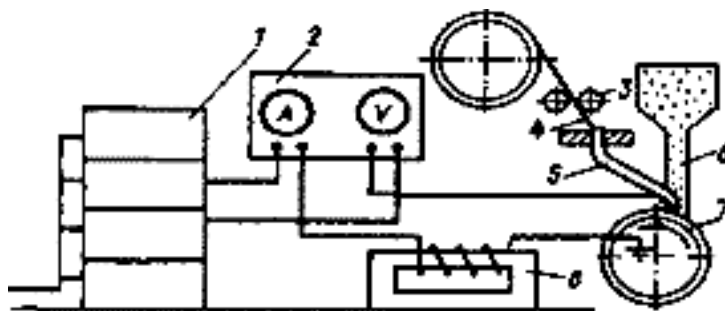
Схема наплавочного апарату А-874Н для автоматичного наплавлення під шаром флюсу
